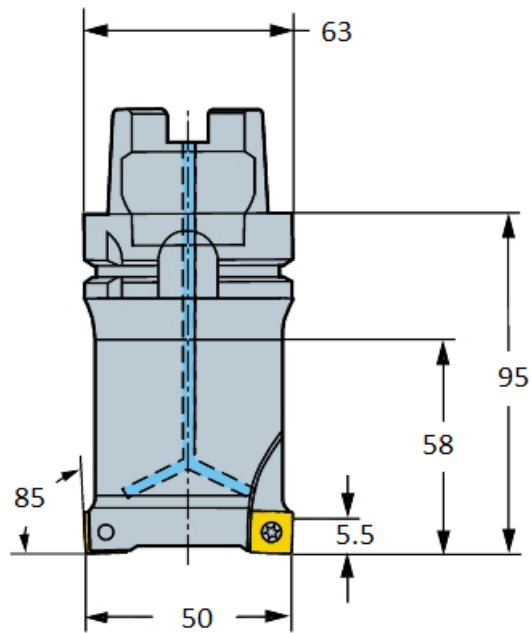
Фреза Sandvik Coromant CoroMill 490-050Q22-14H
